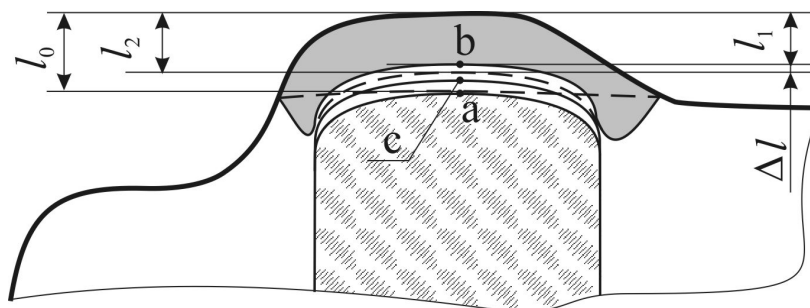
Взаєморозташування герметизуючих елементів затвора: l_0 – початкова товщина прокладки (перед закручуванням); Δl – величина розпрямлення прокладки; а – точка торкання недеформованої прокладки і банки; b – точка завершення закупорювання; с – точка можливого торкання розпрямленої деформованої прокладки і банки під час визначення ступеня безпеки.
